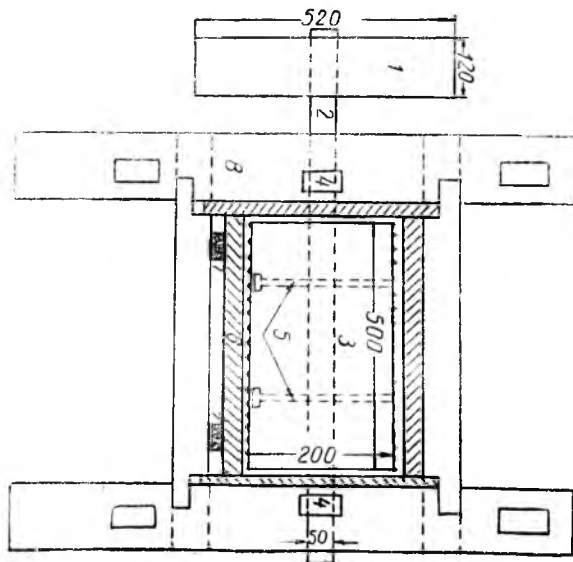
Поперечный разрез (схема) плододробилки конструкции лесничего Мандро. 1 — шкив; 2 — вал; 3 — барабан; 4 — подшипники; 5 — болты; 6 — кожух; 7 — клинья; 8 — станок.
